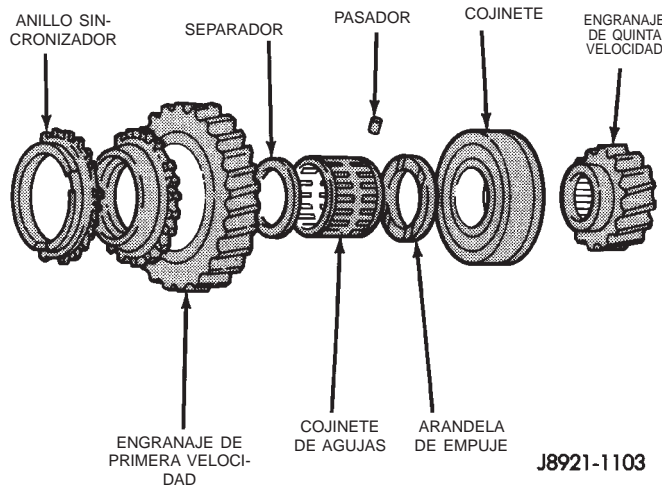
Componentes de engranajes de primera y quinta velocidad
